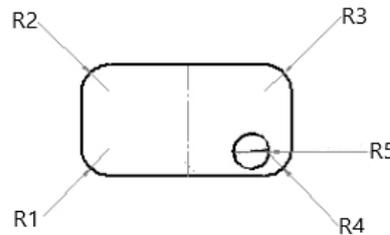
Posisi Pengukuran Presisi Dimensi Objek Sederhana
